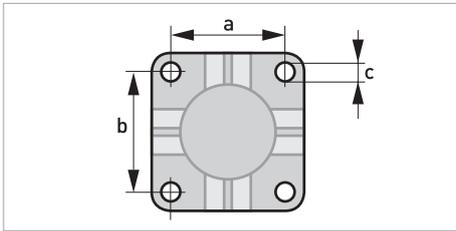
Размеры монтажной пластины корпуса полевого исполнения
